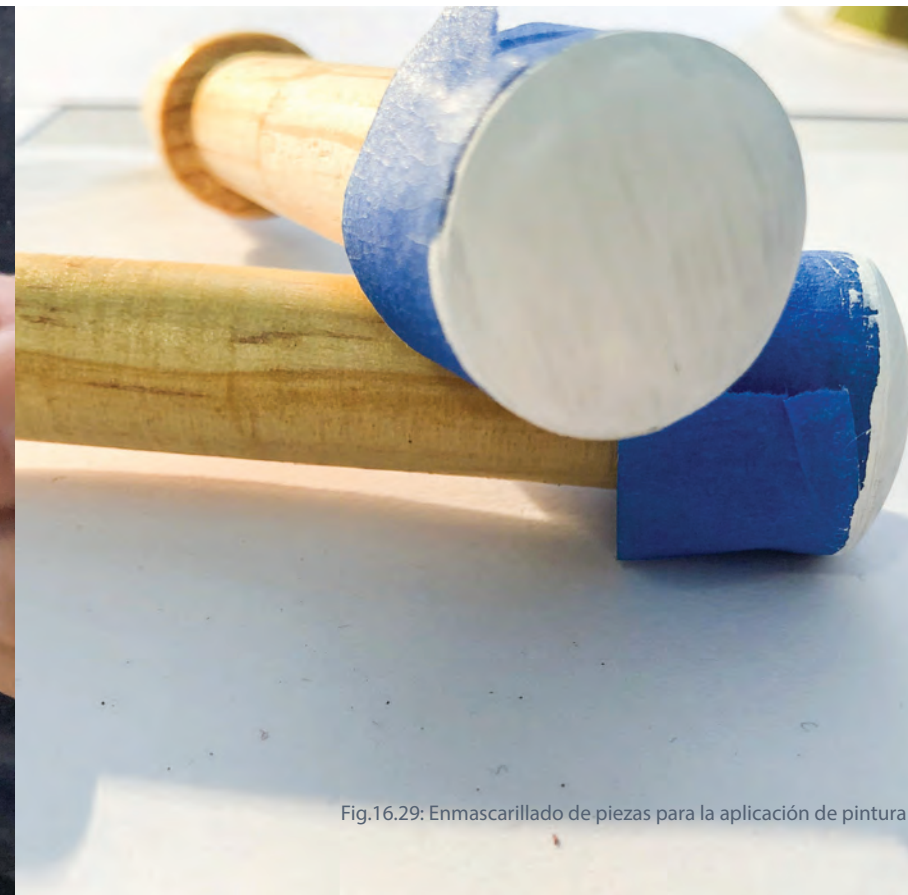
Enmascarillado de piezas para la aplicación de pintura
